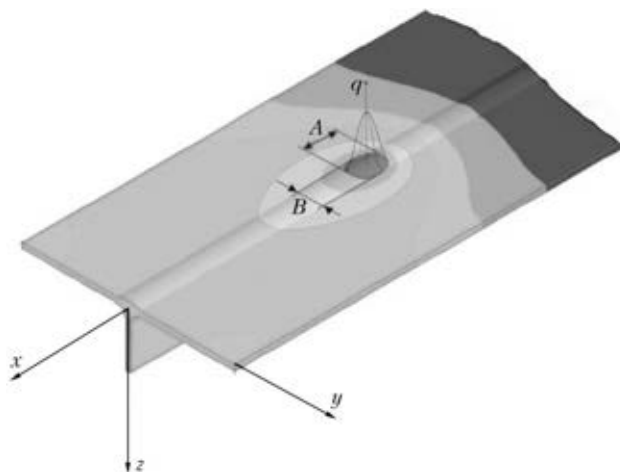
Схема сварочного источника нагрева при сварке образца панели пререзным швом (A — длина сварочной ванны; B — ширина сварочной ванны, q — гауссово распределение тепловой мощности)
